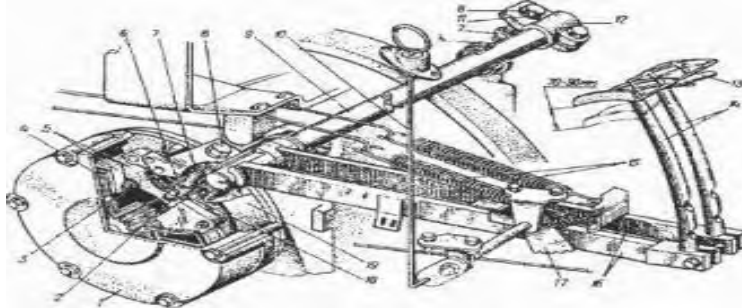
Рабочая тормозная система МТЗ-80, 82
